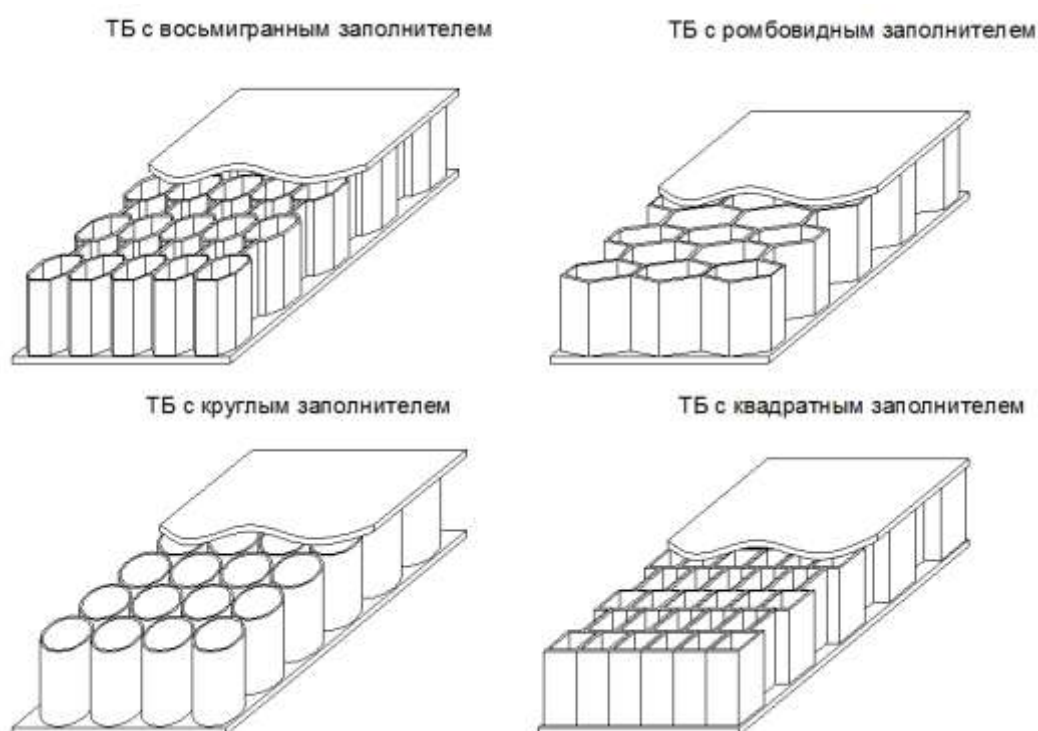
Трехслойные конструкции с сотовыми заполнителями
